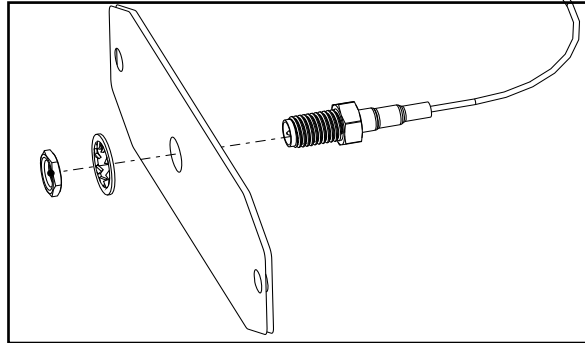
Instalación del conector de antena en la placa de cubierta opcional
